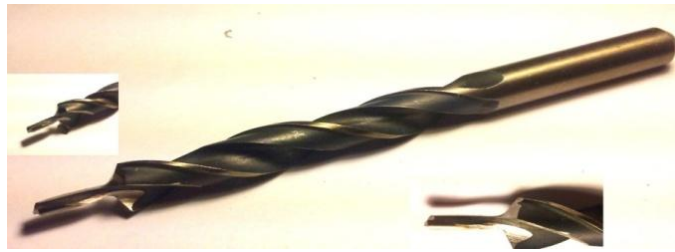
Зображення двохступінчатого свердла для оброблення ПКМ
